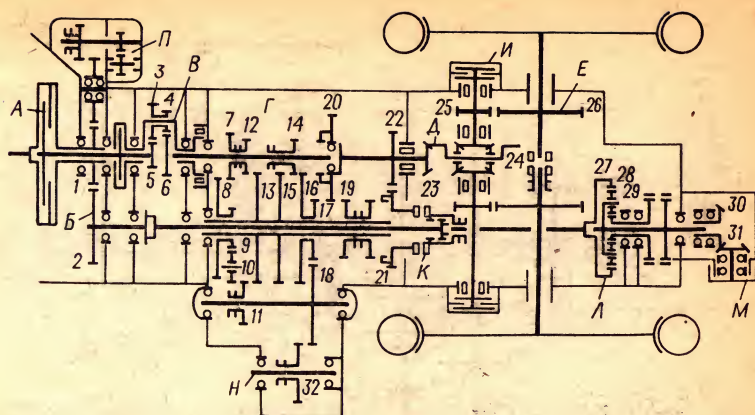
Кинематическая схема силовой передачи трактора МТЗ-50: А — муфта сцепления; Б — независимый привод к ВОМ; В — увеличитель крутящего момента; Г — коробка передач; Д — центральная передача с дифференциалом; Е — конечная передача; И — дисковый тормоз; К — зубчатая муфта переключения ВОМ на независимый и синхронный привод; Л — планетарный редуктор ВОМ; М — приводной шкив; Н — боковой ВОМ; П — привод к насосу гидронавесной системы
